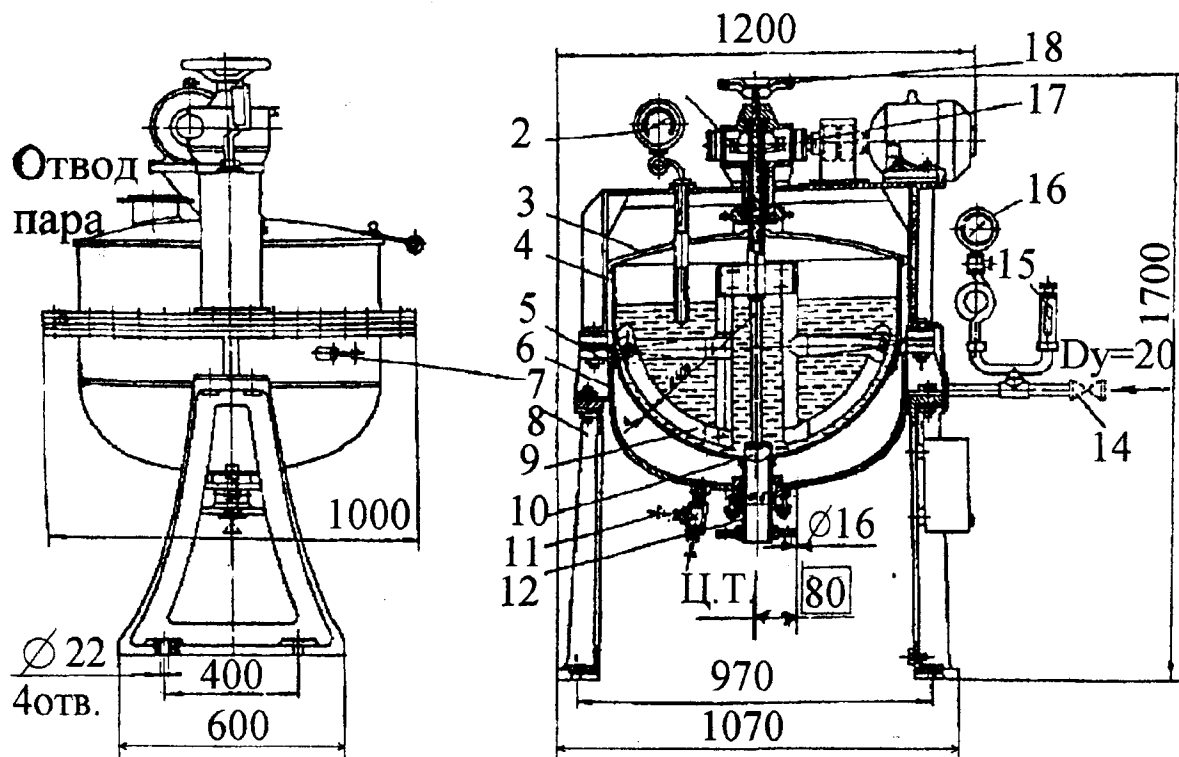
П2. Котёл варочный 28-2А с мешалкой: 1 – червячный редуктор; 2 – термометр; 3 – крышка; 4 – обечайка; 5 – чаша; 6 – паровая рубашка; 7 – кран; 8 –
